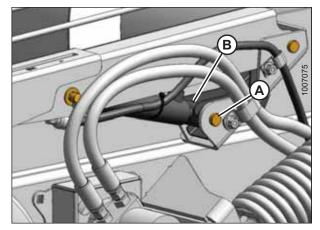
Vérin principal — Côté gauche de la plateforme
